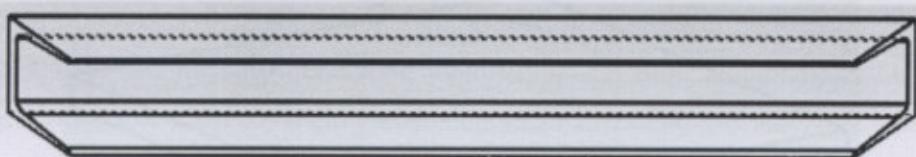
Perfil a 45° , número 1 en la figura anterior. Plano EE-012
